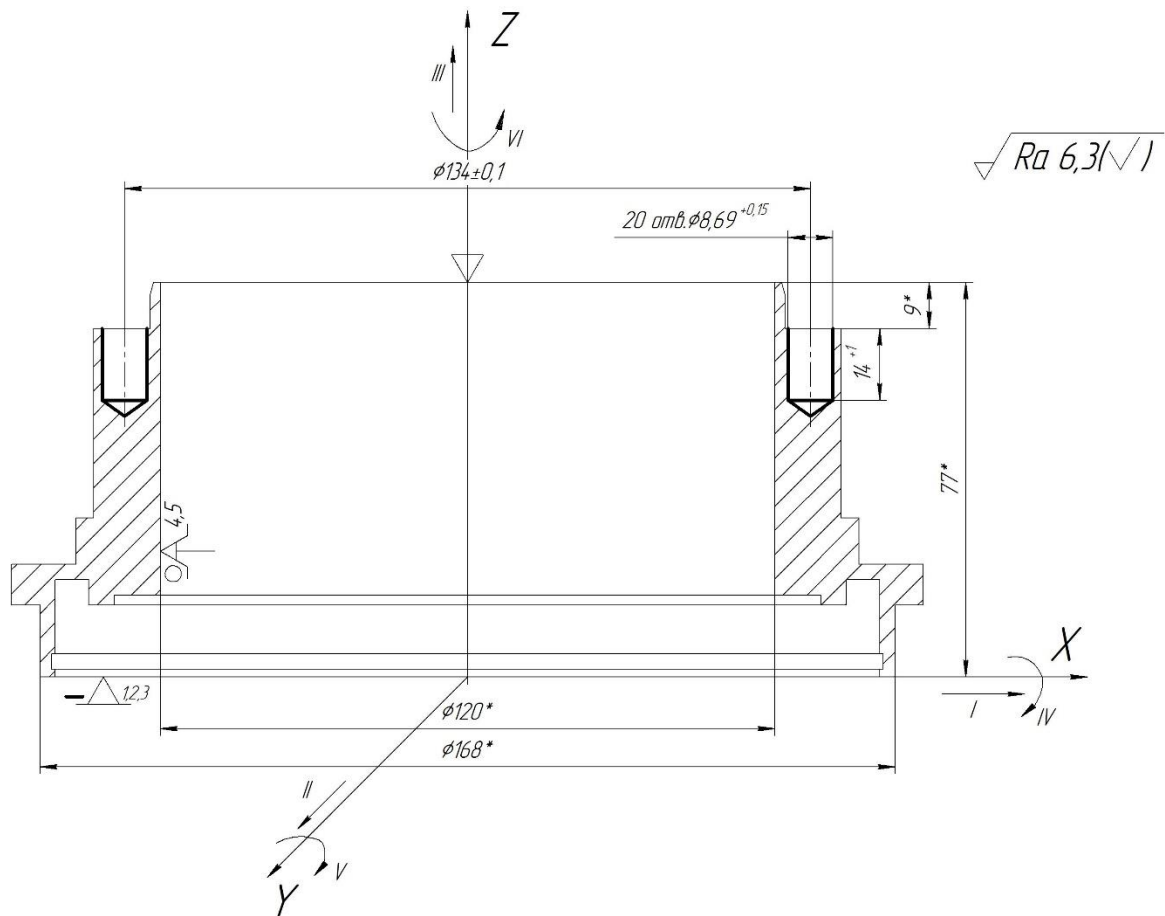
Схема базування заготовки на свердлильній з ЧПК операції
